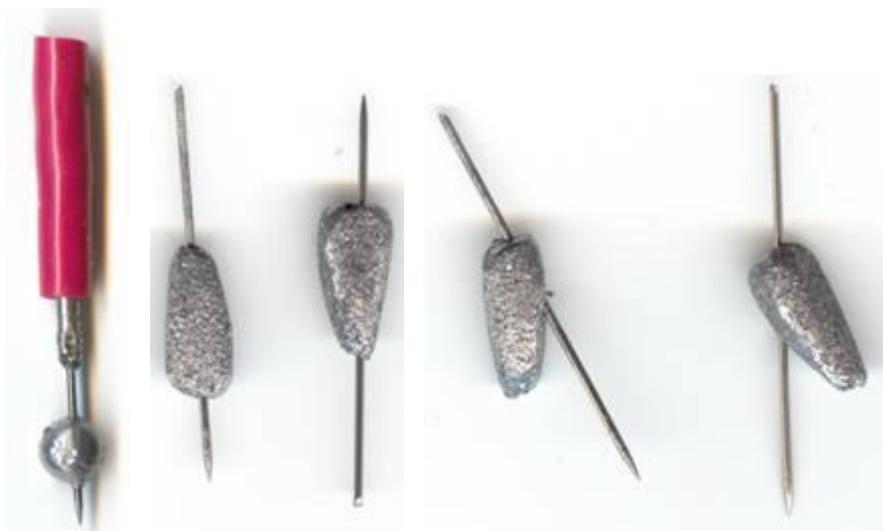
Заготовка тела катаной мормышки: 1- дробинка, проколота мини-шилом, 2 - после раскатки на игле, 3 - после прокола отверстий под леску
